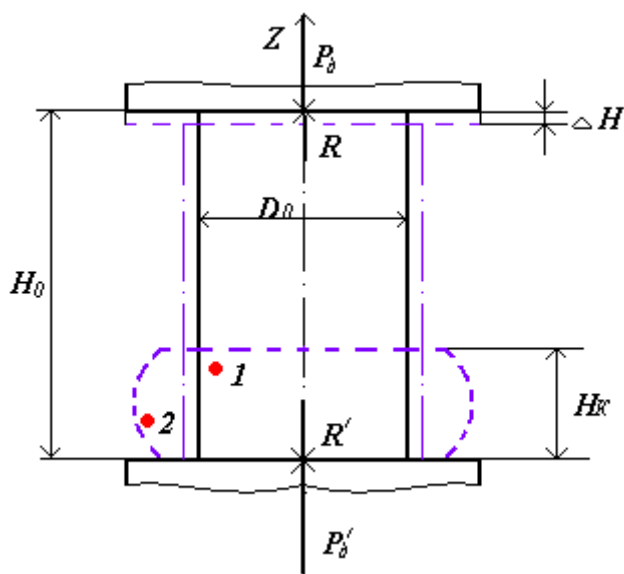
Осадка цилиндрической заготовки на шероховатых плоских бойках.
